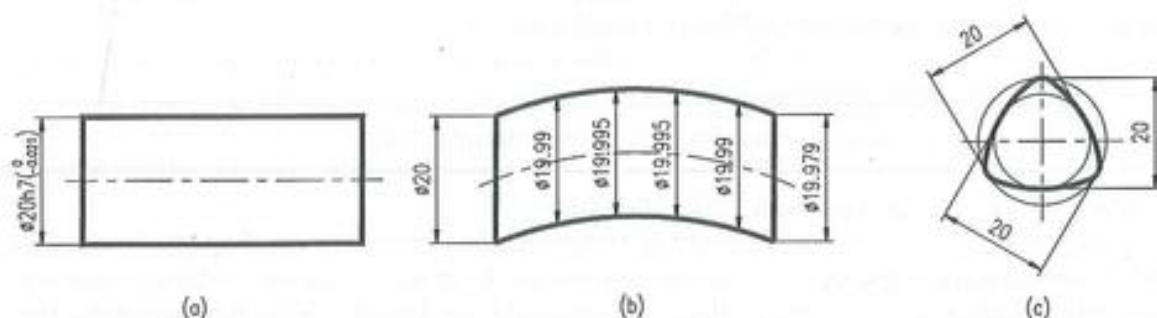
(a) Especificación de tolerancias dimensionales en un cilindro. (b) Dimensiones de una pieza fabricada con errores de rectitud. (c) Dimensiones de una pieza fabricada con defectos de redondez.
